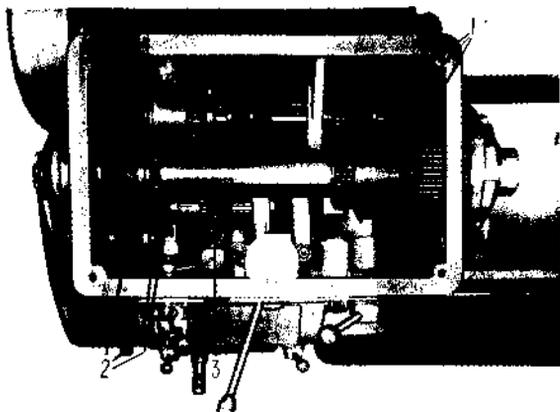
Vista interior del cabezal del torno CUMBRE, Modelo 023. — 1, Engranajes de la reducción. — 2, Mecanismo inversor del avance. — 3, Mecanismo antecaja de avances.
